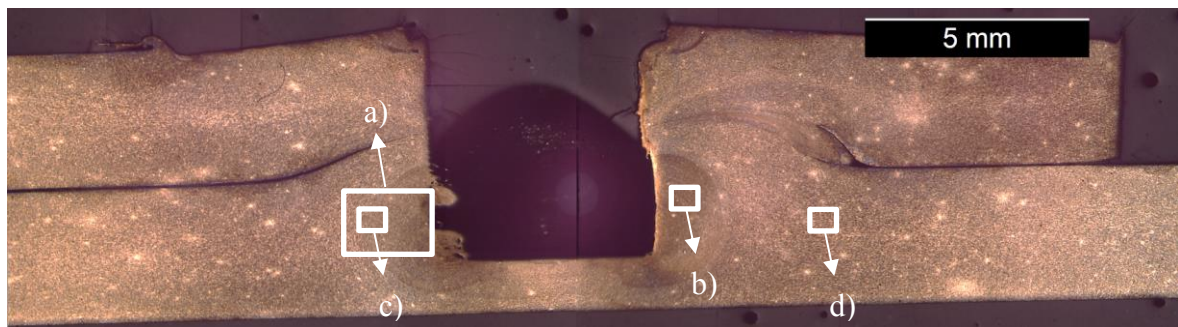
Macrografia do perfil de soldadura do provete S870B-1.
